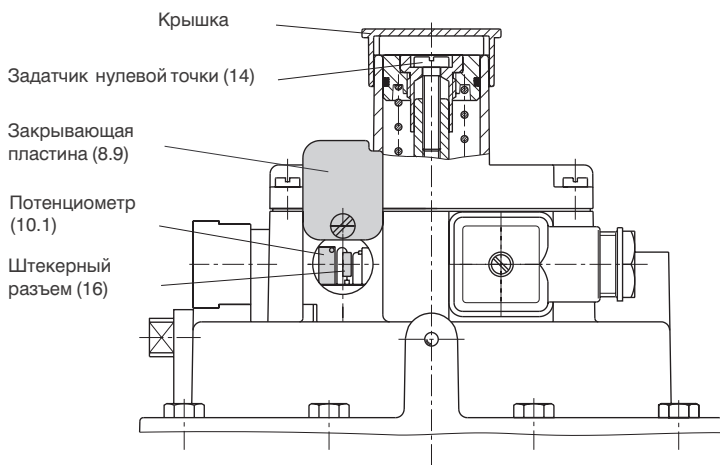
· Сервопривод Тип 3372-032х/034х с вытягивающимся штоком привода
